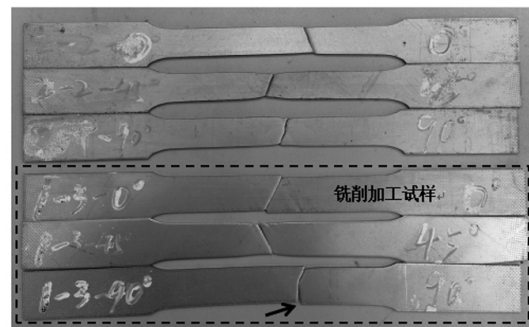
铣削、冲裁加工拉伸试样断裂形式
